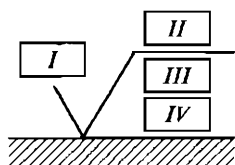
Обозначение шероховатости на чертежах: *I* — параметр шероховатости; *II* — вид обработки и другие дополнительные указания; *III* — базовая длина; *IV* — обозначение направления неровностей
